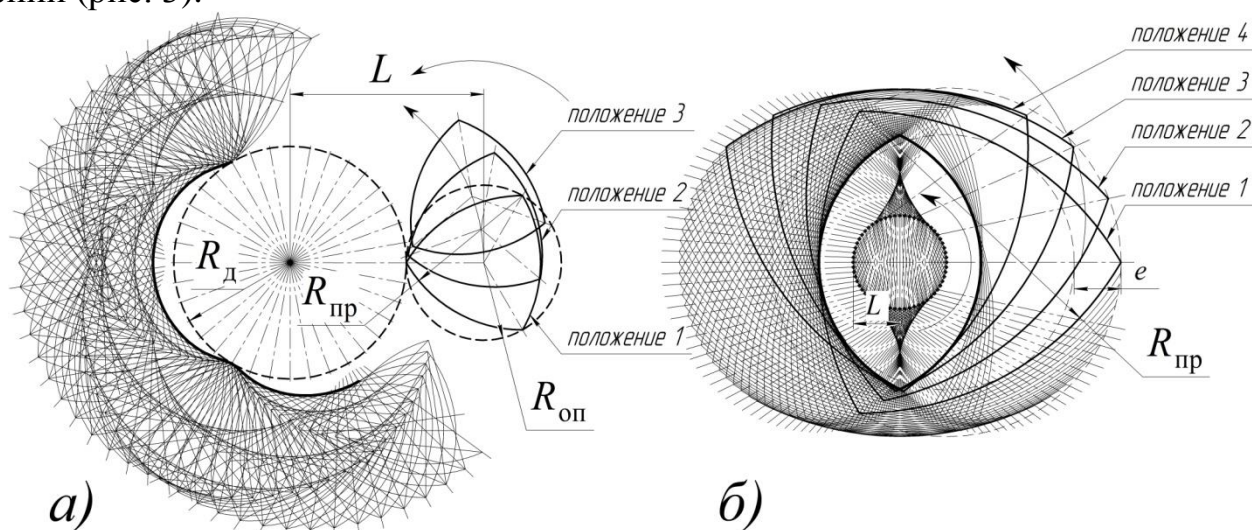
Схема построения профиля долбяка для обработки: а – вала; б – втулки
